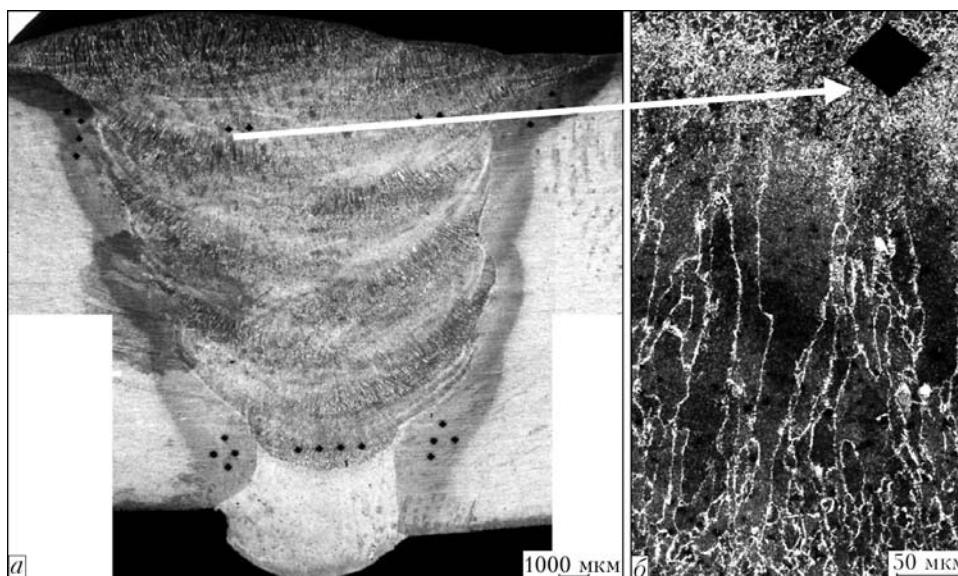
Макро- (а) и микрошлиф (б) многослойного сварного соединения, выполненного металлопорошковой проволокой POWER BRIDGE 60M (наблюдается подавление роста кристаллитов на начальной стадии их роста)
